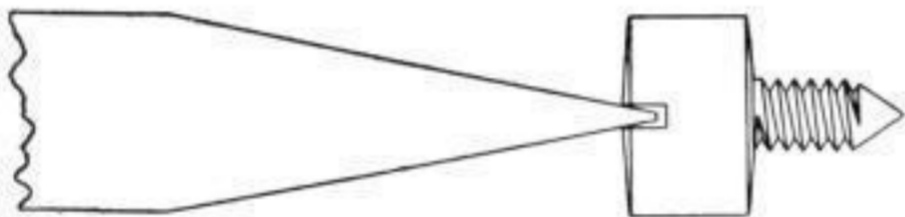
Schraubenzieher im Einschnitt der Schraube.
